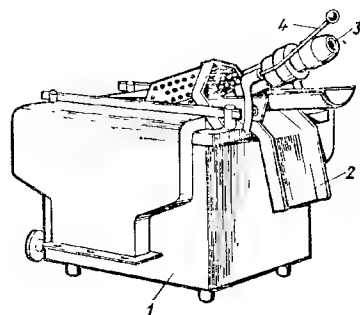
Колокольная ванна типа ВК-40: 1 — корпус ванны; 2 — лоток; 3 — электродвигатель для вращения колокола; 4 — ручка для подъема и опускания колокола
